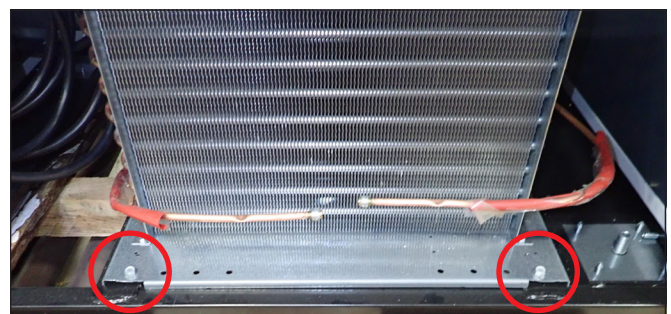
Position der Schrauben des hinteren Lüftungsgitters. Das Gitter vorsichtig abnehmen.
